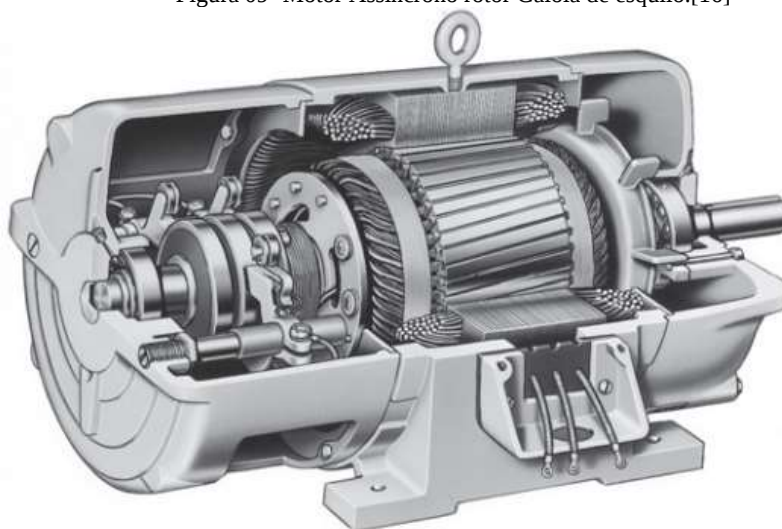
Motor Assíncrono de Rotor Bobinado. [16]
